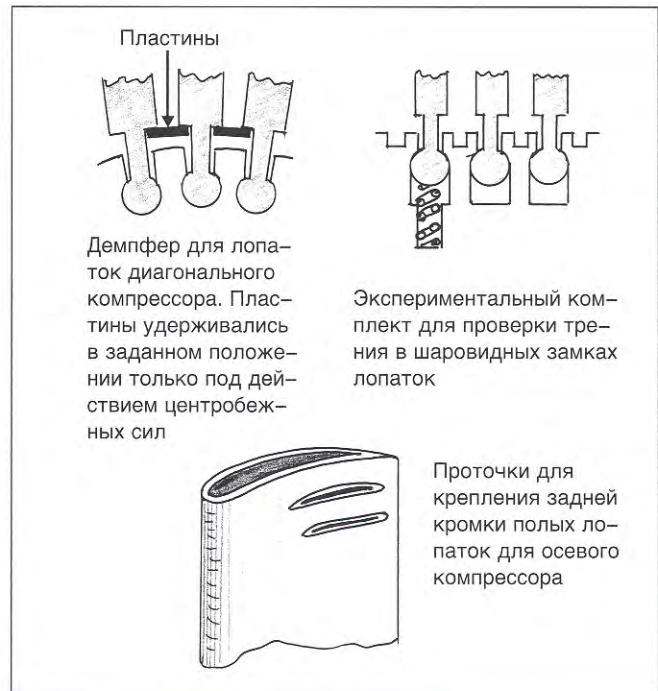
Экспериментальные лопатки компрессора для двигателя HeS 011 (109-011)
